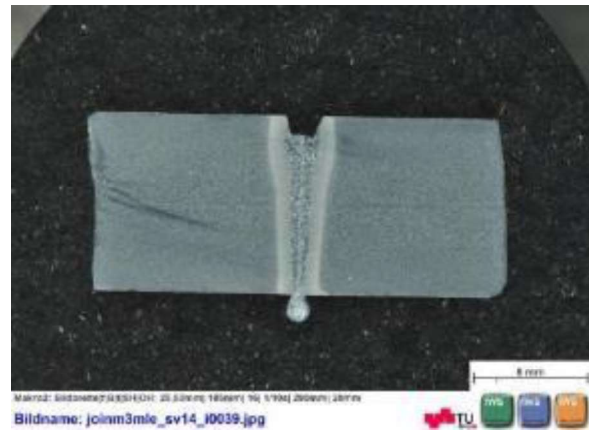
Blindschweißung geätzt aus Probe 4.1,  $I=20 \text{ mA}$ ,  $v=10 \text{ mm/s}$
